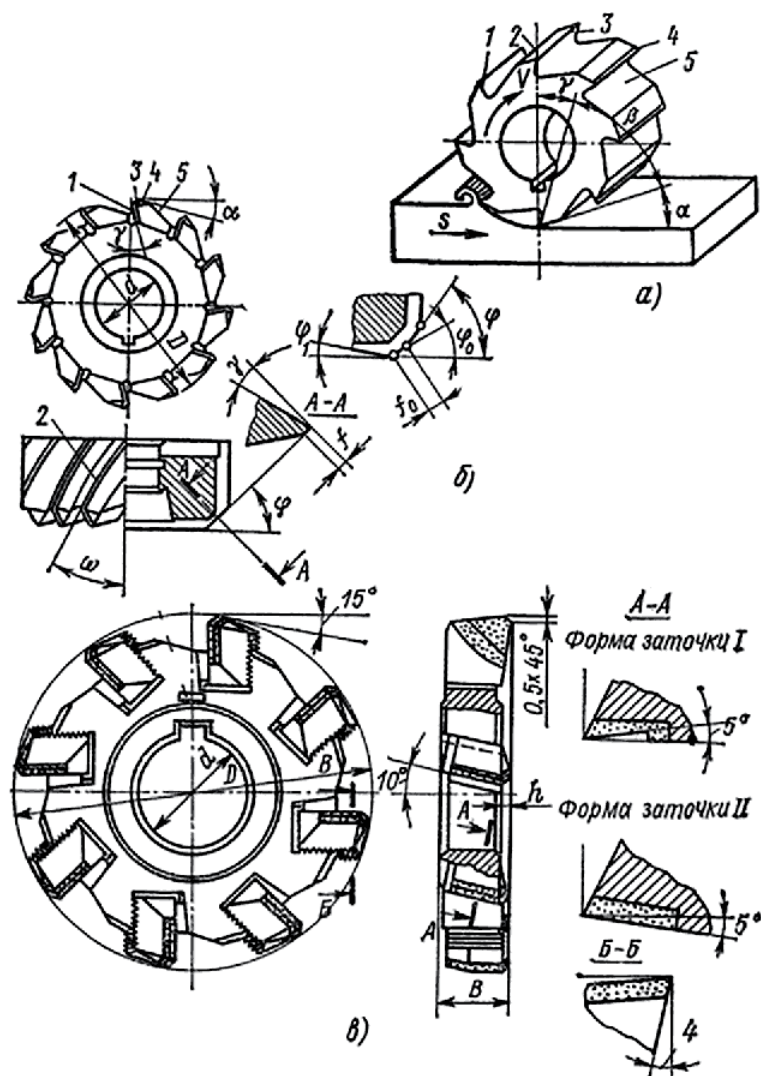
Элементы поверхности и геометрические параметры цилиндрической фрезы с прямыми (а), винтовыми (б) зубьями, со вставными твердосплавными ножами (в)
